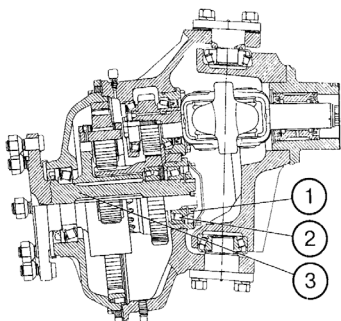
Проверка зазоров в подшипниках передних колес:
